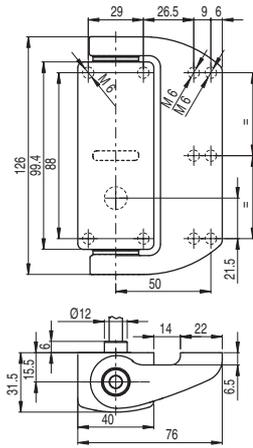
Dimensions des S420-9CB2-LW et S420-OS-CB2-LW en mm
